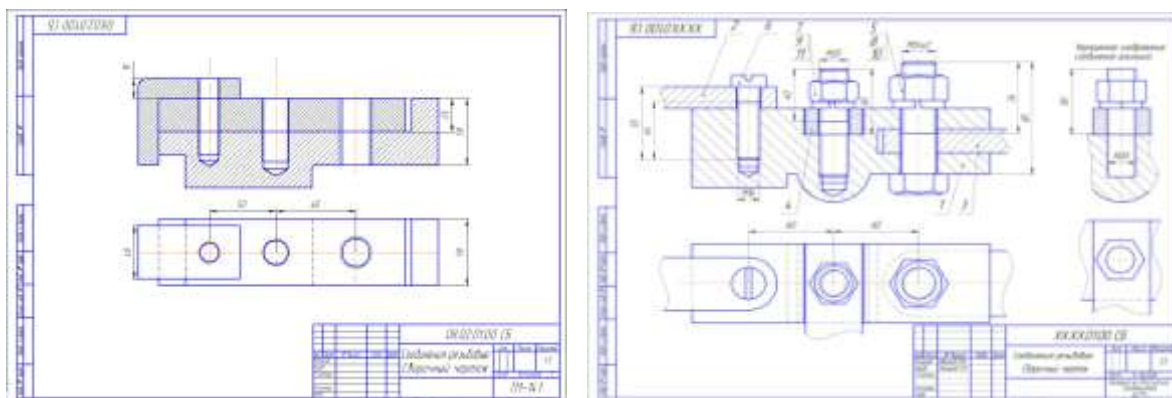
Задание и сборочный чертеж «Изделия резьбовые и резьбовые соединения»
